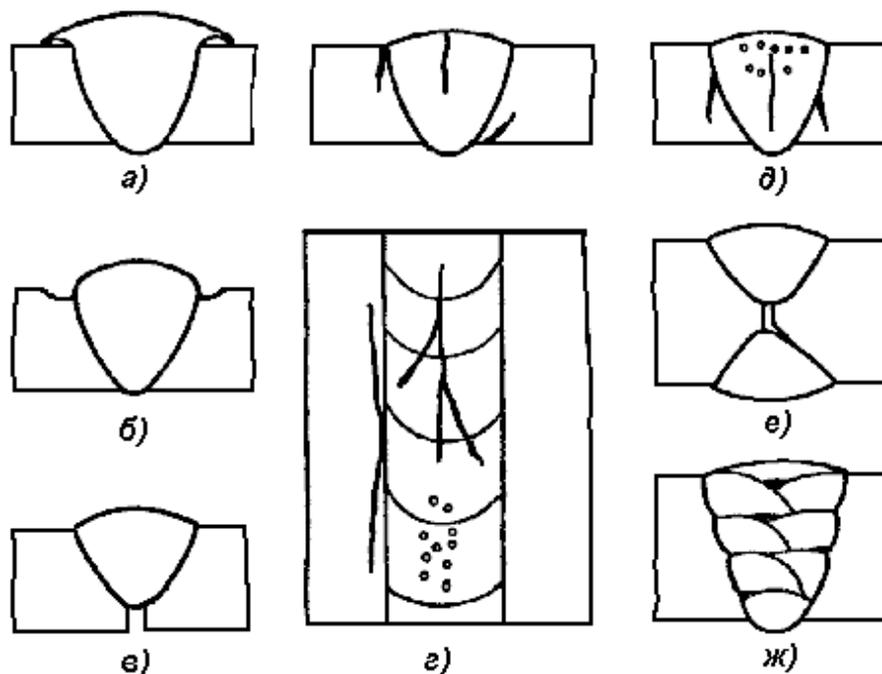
Виды дефектов в сварных соединениях
